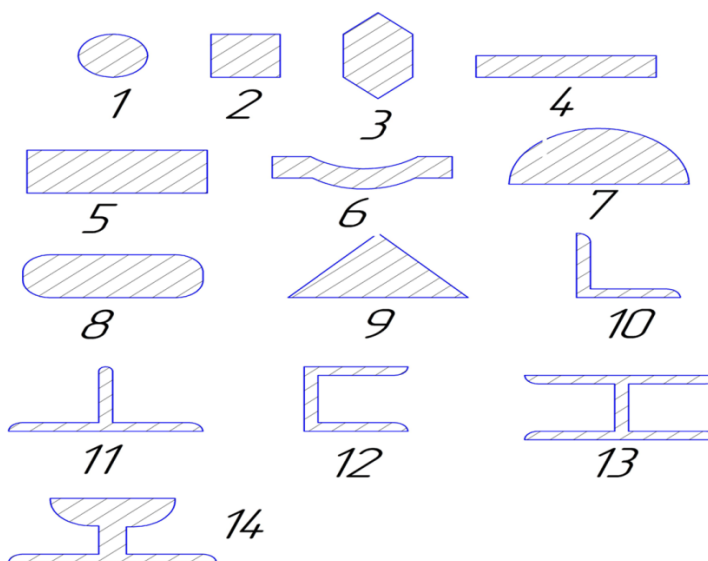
Различные профили металла. Где 1- круг; 2 -квадрат; 3- шестигранник; 4- полоса; 5- лист; 6 - рессора; 7- сегмент; 8-овал; треугольник; 11 тавровая балка; 12 - швеллер; 13 - двутавровая балка; 14-рельс.[3]
